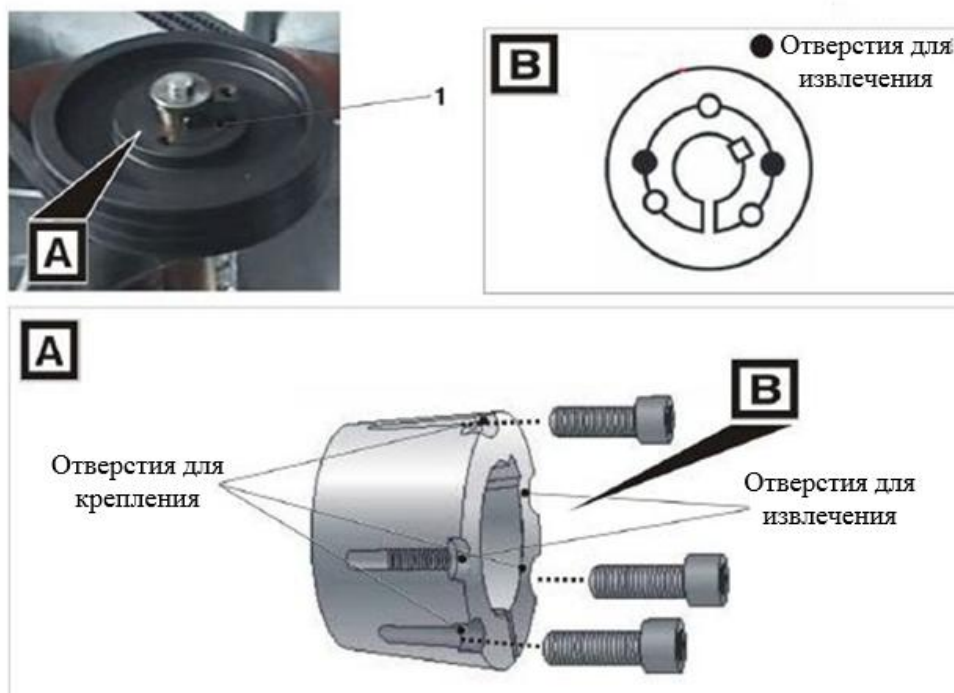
Детализовка конической втулки с обозначением мест установки болтов
